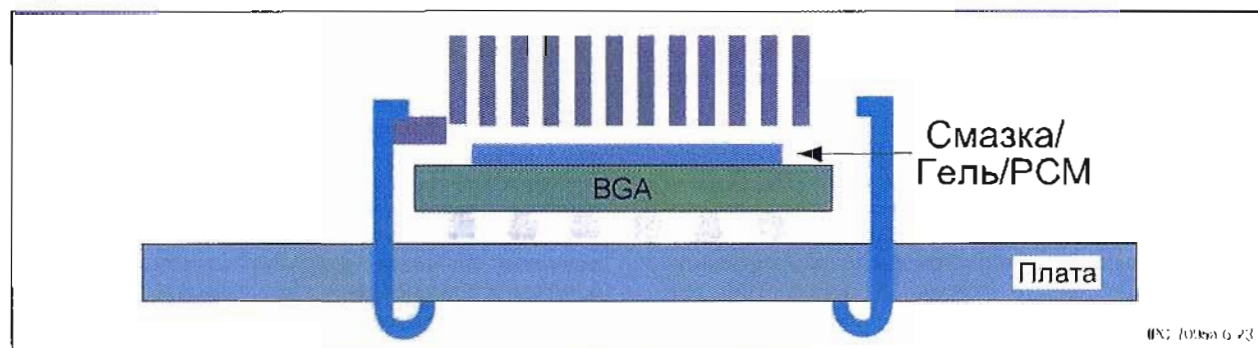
Радиатор, установленный на корпус BGA при помощи зажимов, крепящихся в отверстиях печатной платы
